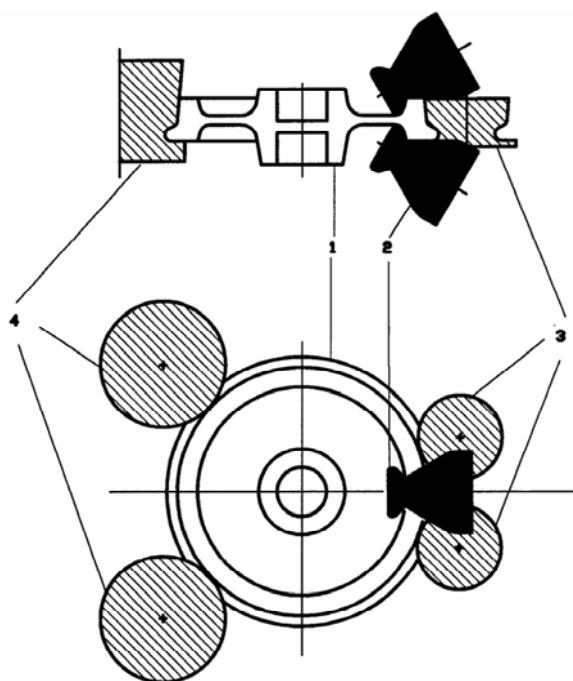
Схема прокатки колеса на колесопрокатном стане:
